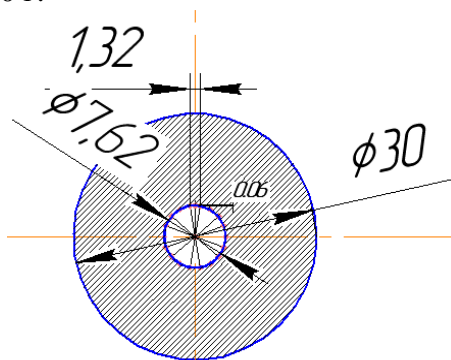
Поперечное сечения ствола винтовки образца 1891/30г. с полигональным профилем
